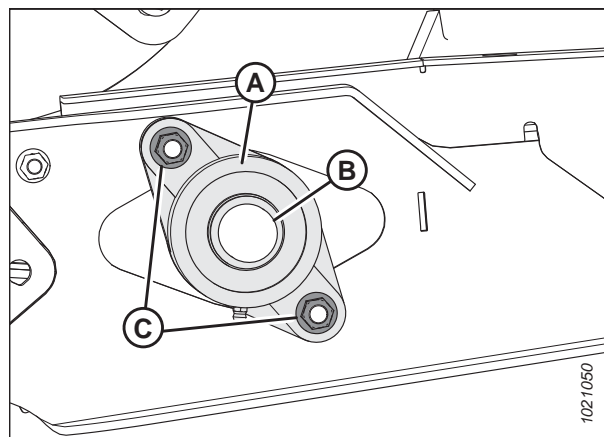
Подшипник приводного ролика подающего полотна
